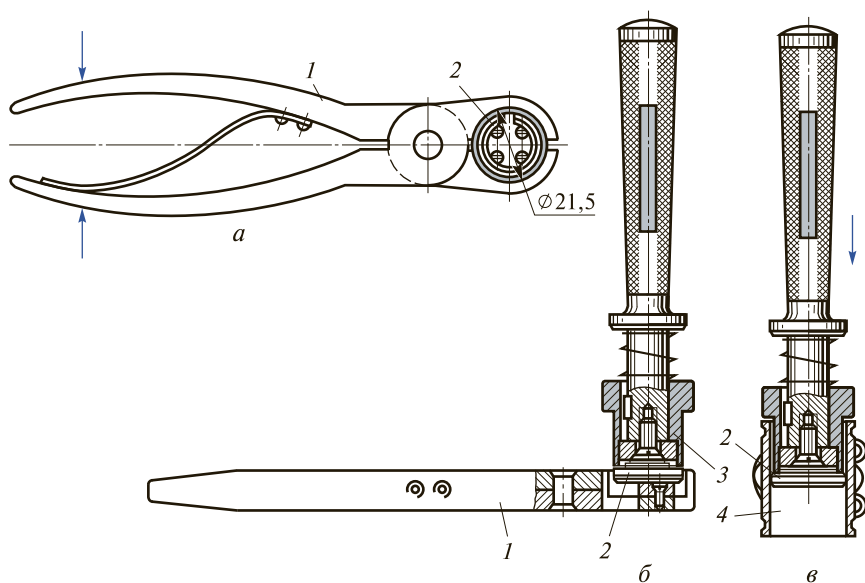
Установка опорного кольца автоматического устройства в колесный цилиндр:
